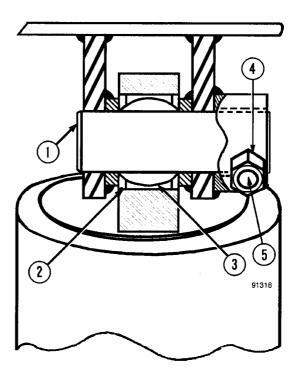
MONTAJE SUPERIOR DEL CILINDRO DE ELEVACIÓN
